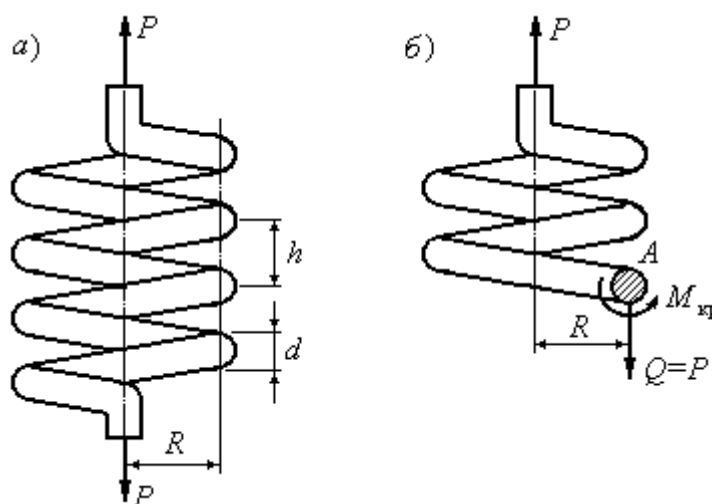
Цилиндрическая пружина с малым шагом витка
